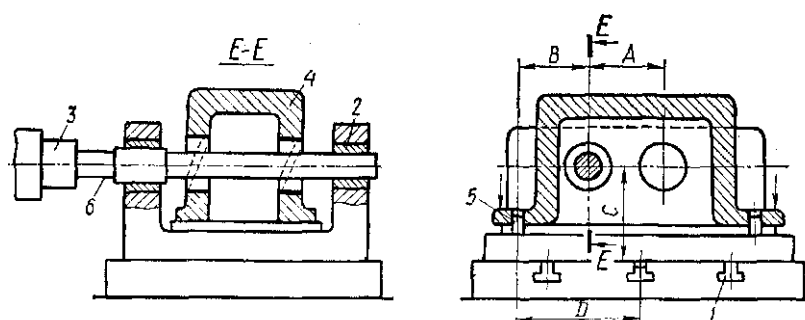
Розточування отворів за допомогою напрямних втулок: 1 - настановні шпонки; 2 - напрямні (кондукторні) втулки; 3 - шпиндель; 4 - деталь; 5 - настановні пальці; 6 - борштанга (оправлення).
